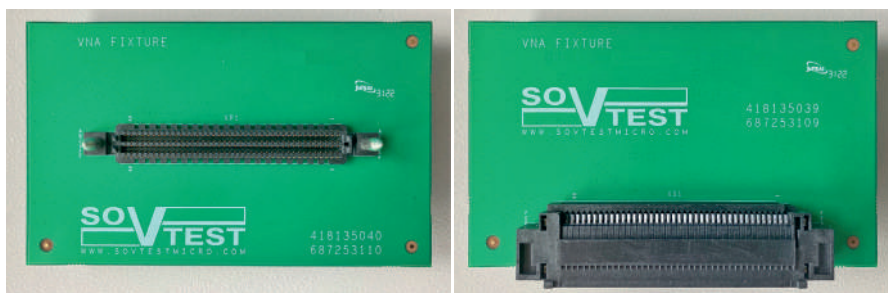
Измерительная оснастка ООО «Совтест Микро», вид сверху. Слева: плата соединителя вилка. Справа: плата соединителя розетка
